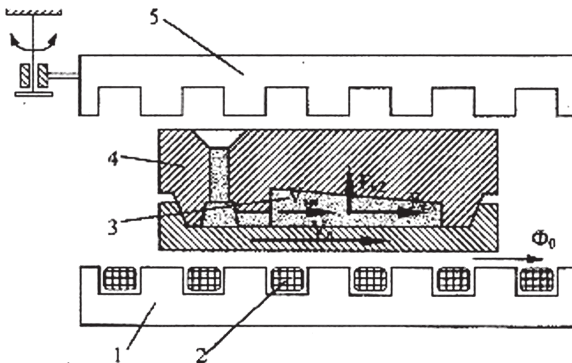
Технологическая схема МГД-устройства для электромагнитной обработки металла в литейной форме бегущим магнитным полем: 1 - магнитопровод активного индуктора; 2 - обмотки; 3 - отливка; 4 - литейная форма; 5 - пассивный магнитопровод
